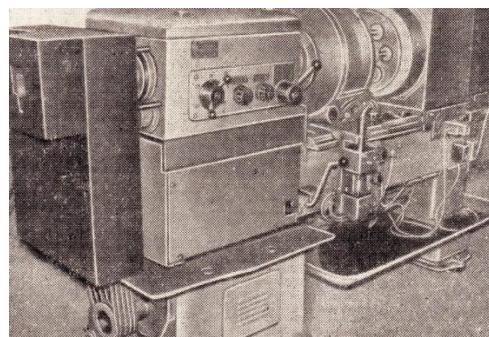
Внешний вид экспериментального стенда на базе токарного станка 1К62 для алмазно-электролитической обработки одновременно 6 долотчатых коронок типа КДП
